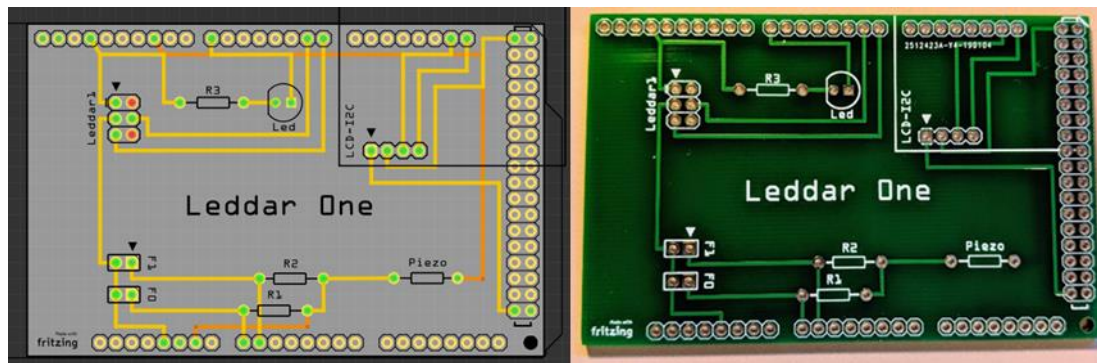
Diseño en Fritzing de la placa para su impresión y placa PCB impresa.
